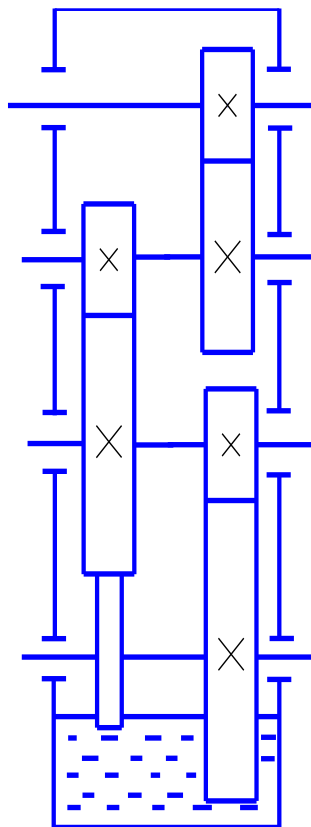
Схема мастила редуктора ВКУ-950
